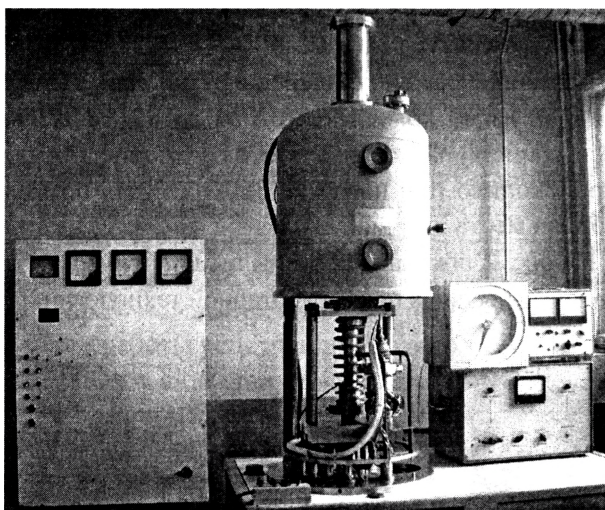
Установка для импульсной диффузионной сварки в вакууме
